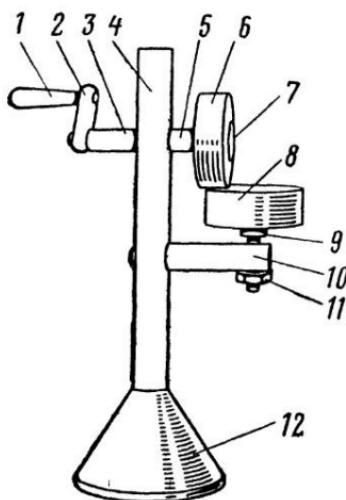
Модель фрикционной передачи с перпендикулярными осями дисков: 1 — ручка; 2 — рычаг ручки; 3 — упорная втулка; 4 — стойка; 5 — вал привода; 6 — ведущий диск; 7 — металлическая втулка; 8 — ведомый диск; 9 — ось ведомого диска; 10 — кронштейн; 11 — контргайка; 12 — основание.
